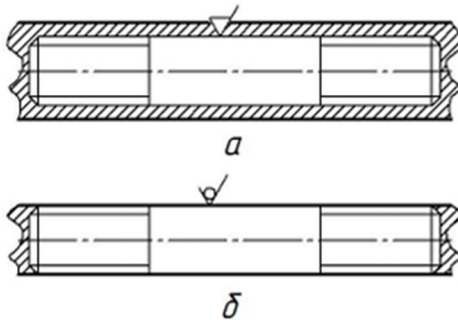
Шпилька, виготовлена обробленням різанням (а)
